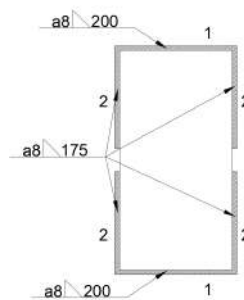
Soldaduras en la chapa (mm)
